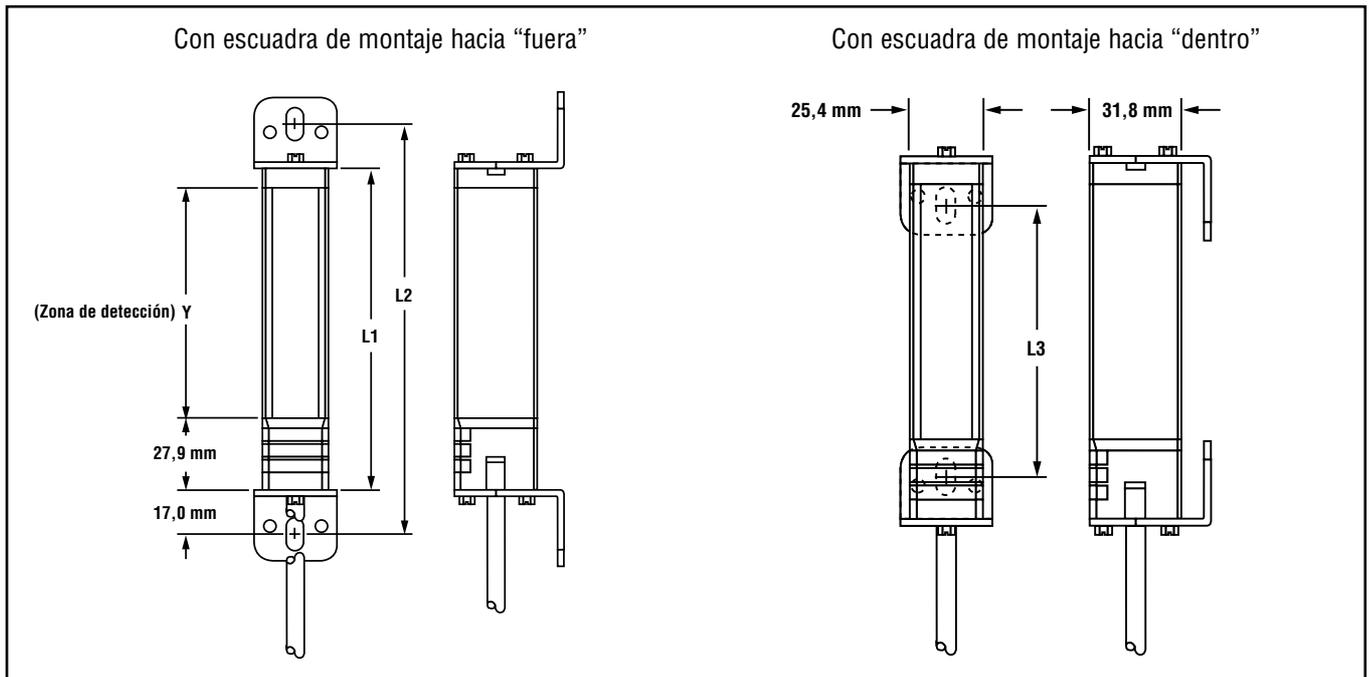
Dimensiones de montaje de emisor y receptor y posición de la zona de detección
